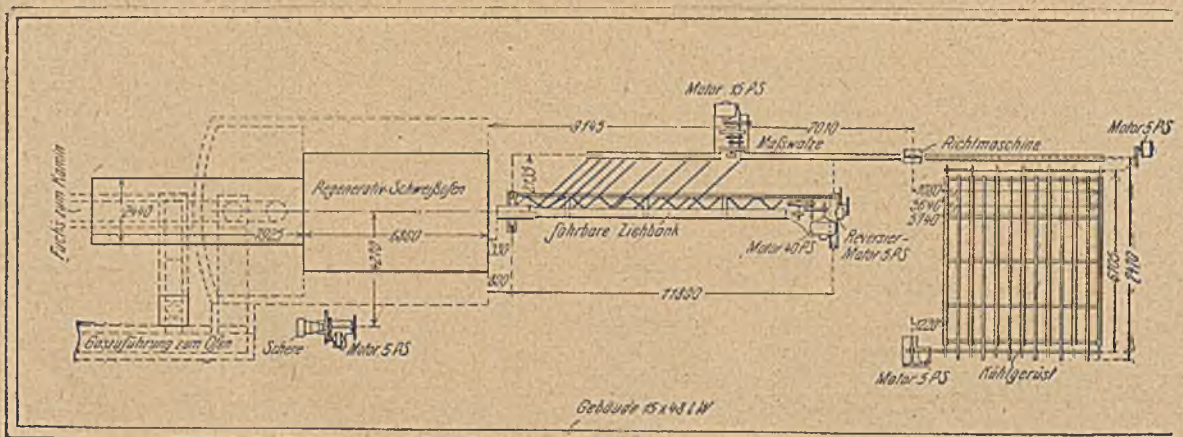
Gasrohr-Schweißwerk.
